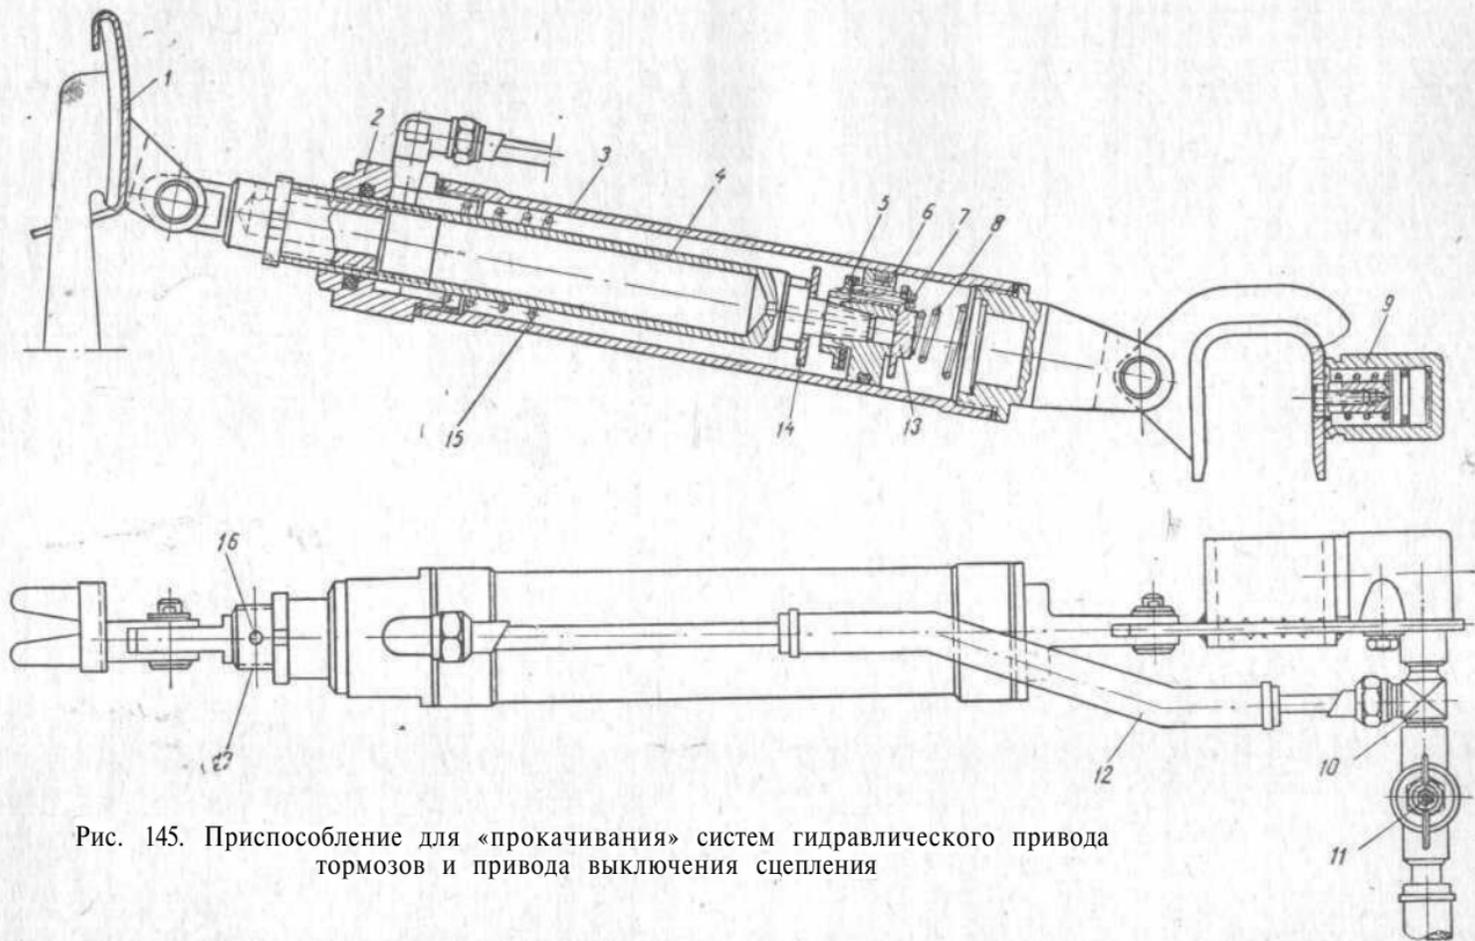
Приспособление для «прокачивания» систем гидравлического привода тормозов и привода выключения сцепления
